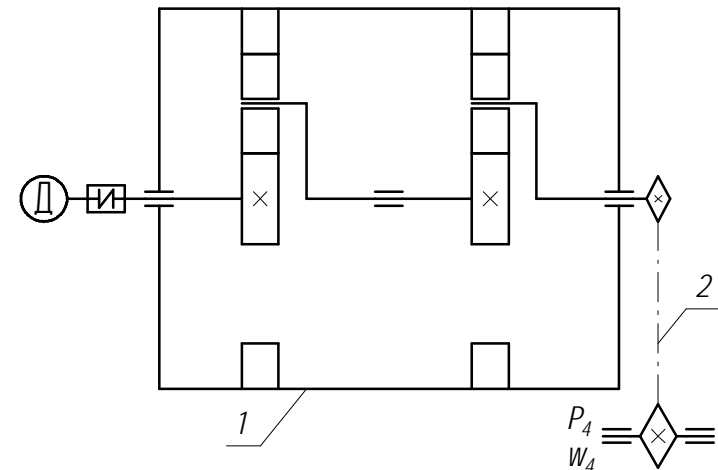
Схема привода с планетарным двухступенчатым редуктором.
